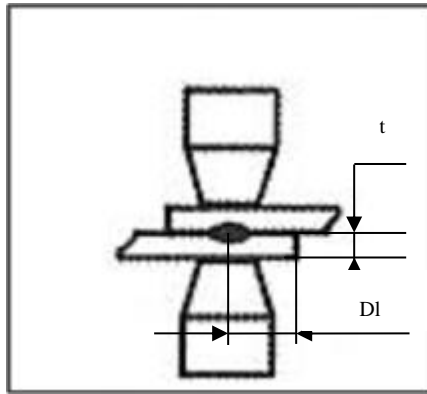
Relación entre la ubicación del punto de soldadura y el borde de la hoja de metal.
